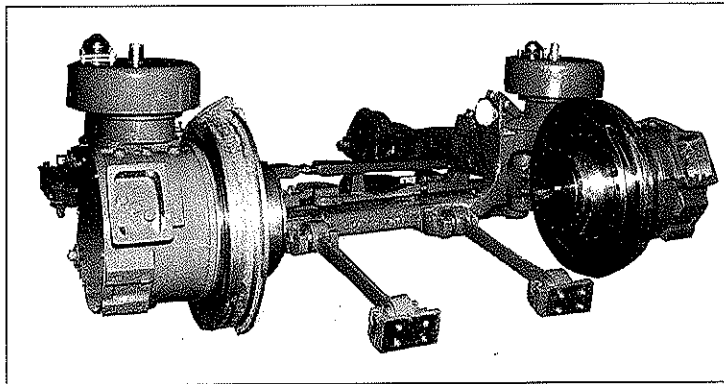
Das Drehgestell von der Motorseite gesehen. Mit Hinweis auf die Lenker mit dem Wagenkasten und die Drehpunkte der Rad/Motorgruppe
